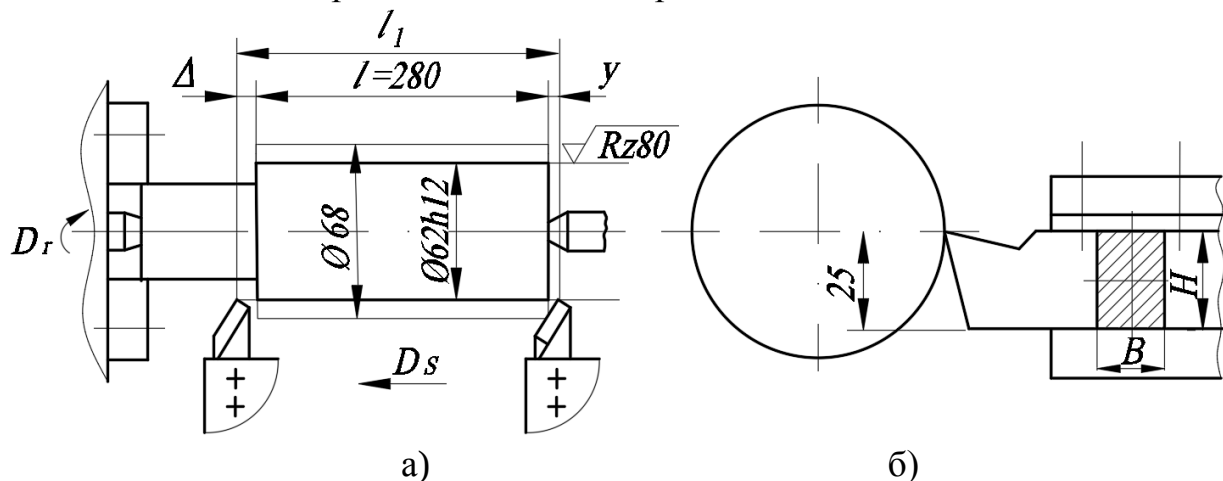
Ескізи обробки (а) і встановлення різця (б)
